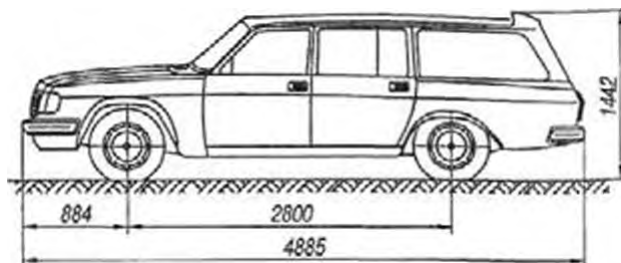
Автомобиль "Волга" ГАЗ-31022 и его габаритные размеры
